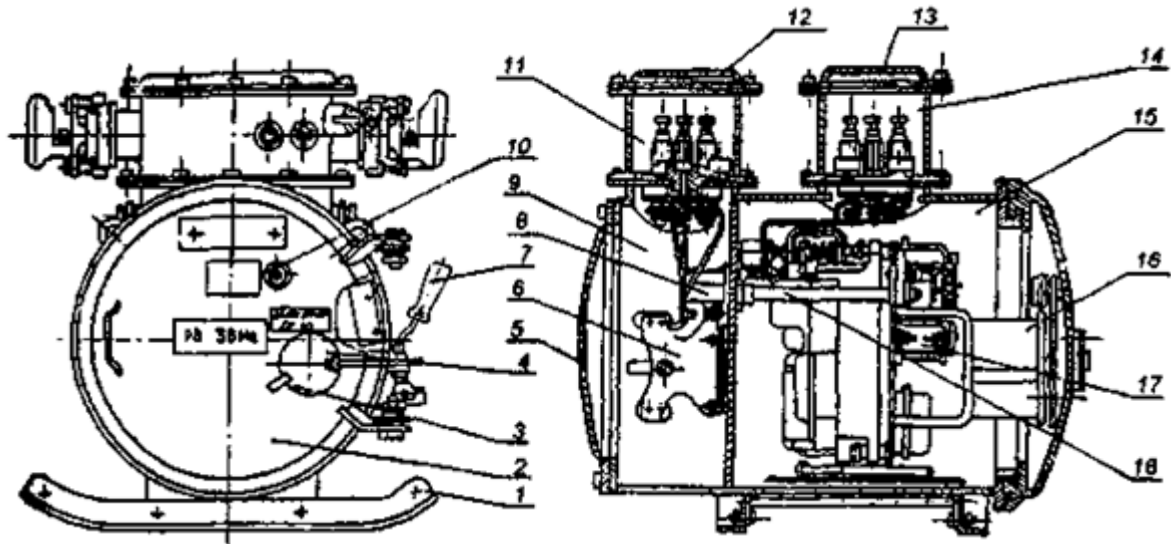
Общий вид пускателя ПВИ-250БТ: 1 – салазки; 2 – крышка; 3 – привод замка быстрооткрываемой крышки; 4 – блокировочная скоба; 5 – крышка отделения разъединителя; 6 – разъединитель; 7 – рукоятка привода разъединителя; 8 – трансформаторы тока; 9 – отделение разъединителя; 10 – смотровое окно; 11 – сетевое отделение; 12 – крышка сетевого отделения; 13 – крышка отделения выводов; 14 – отделение выводов; 15 – контакторное отделение; 16 – панель аппаратуры; 17 – блок контакторный; 18 – направляющая контакторного блока
